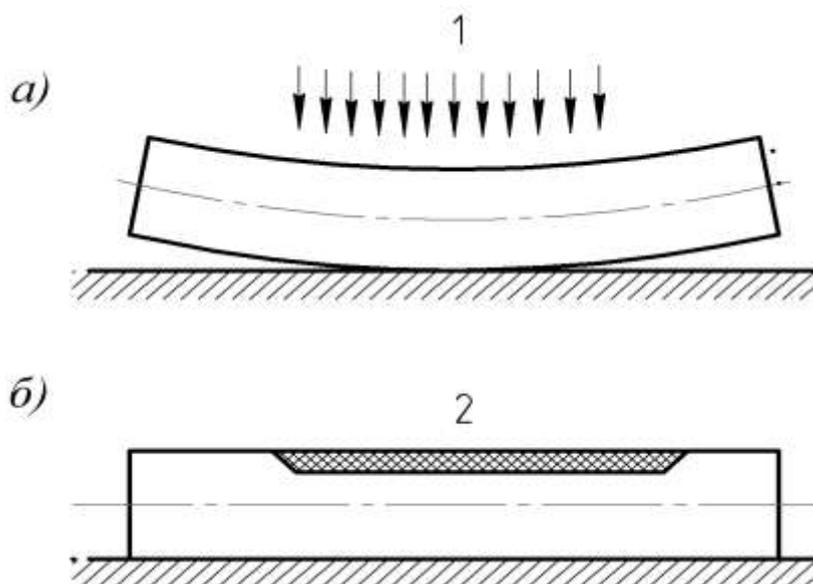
Схема правки поверхностным наклепом: *а* – до наклепа; *б* – после наклепа; 1 – поверхностный наклеп; 2 – наклепанный слой
